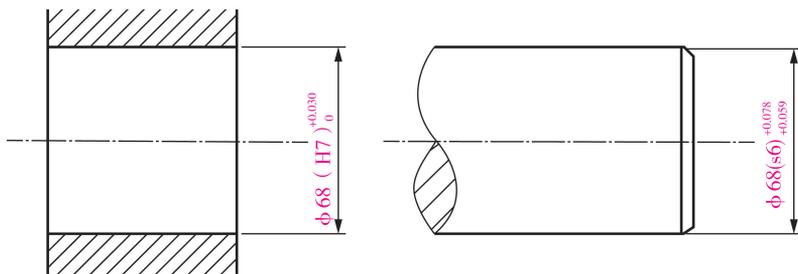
孔和轴的公差带在零件图上的标注
